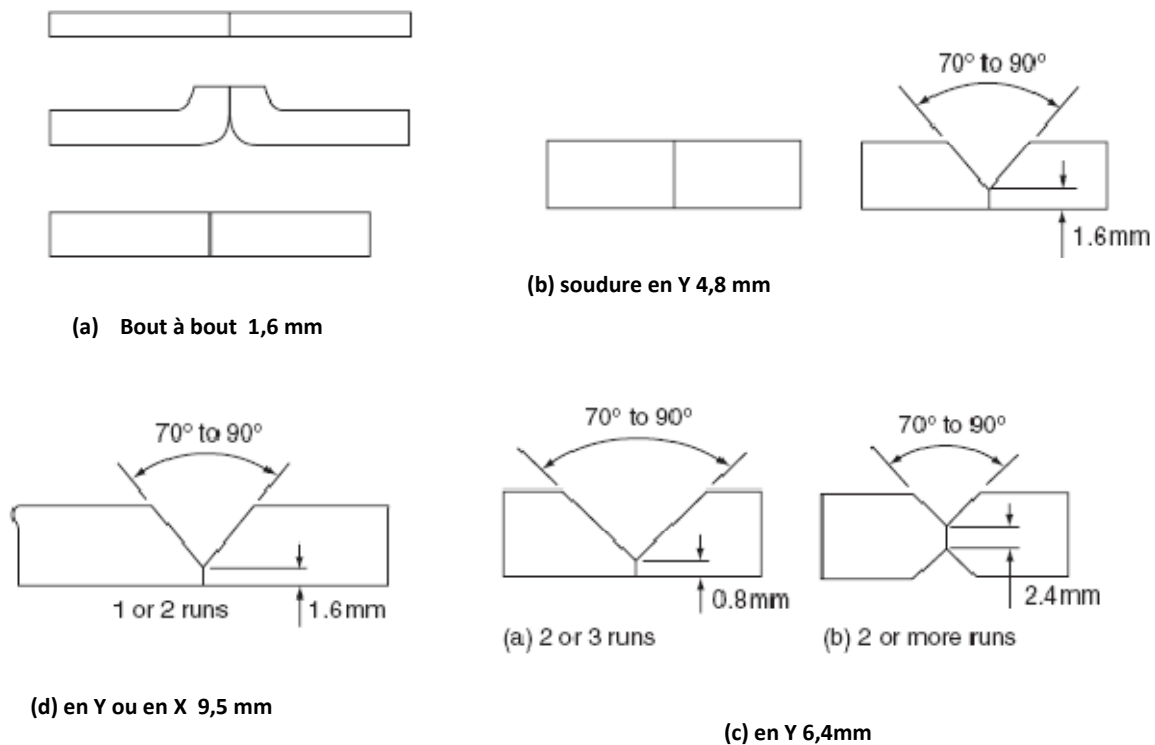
Règle de préparation des bords pour soudage TIG [31]
